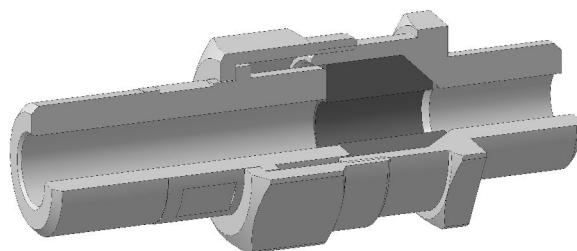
Конструкция кабельного ввода ВН с фитингом для монтажа кабеля в трубе
